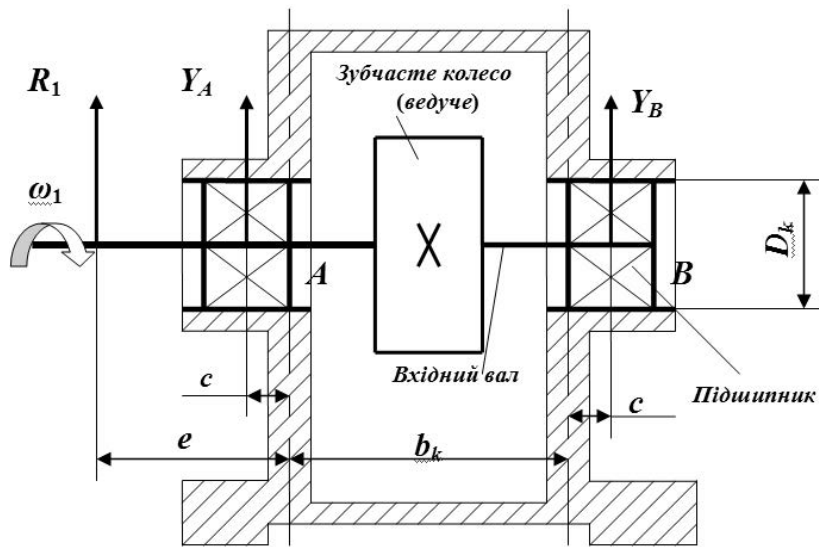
Поперечний переріз корпусу редуктора та схема його навантаження
